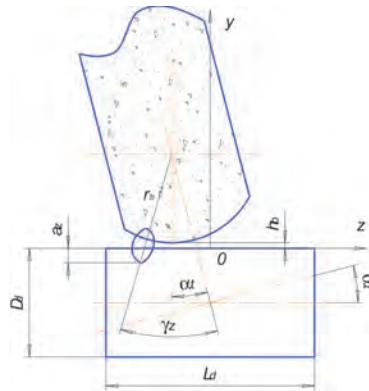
Схема способа многобрускового формообразующего суперфиниширования
